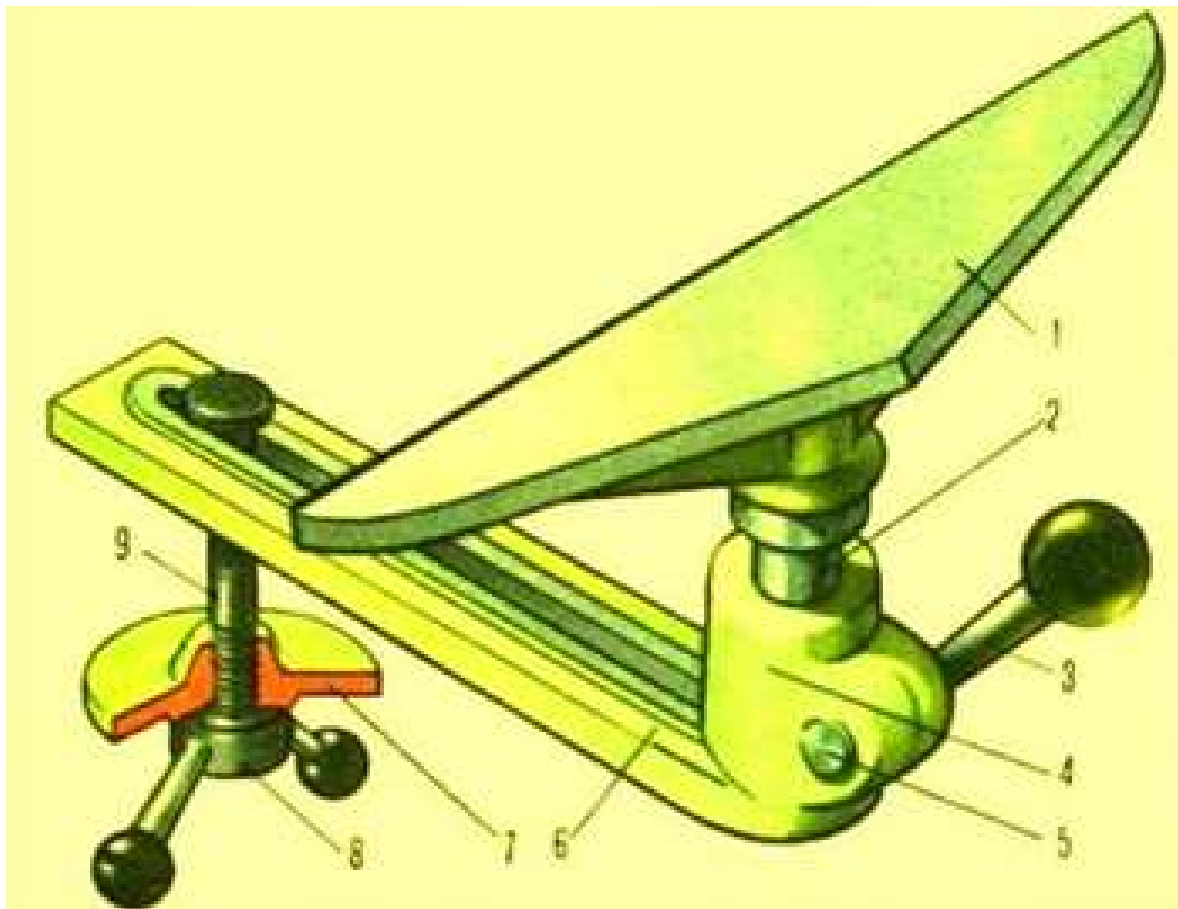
Підручник з тримачем 1-похиле ложе 2-стрижень 3-рукоятка стопора 4-порожниста втулка 5-стопор 6-брус з прорізом 7 — притиск 8 — гайка з рукоятками 9 — болт з квадратною підголовкою
